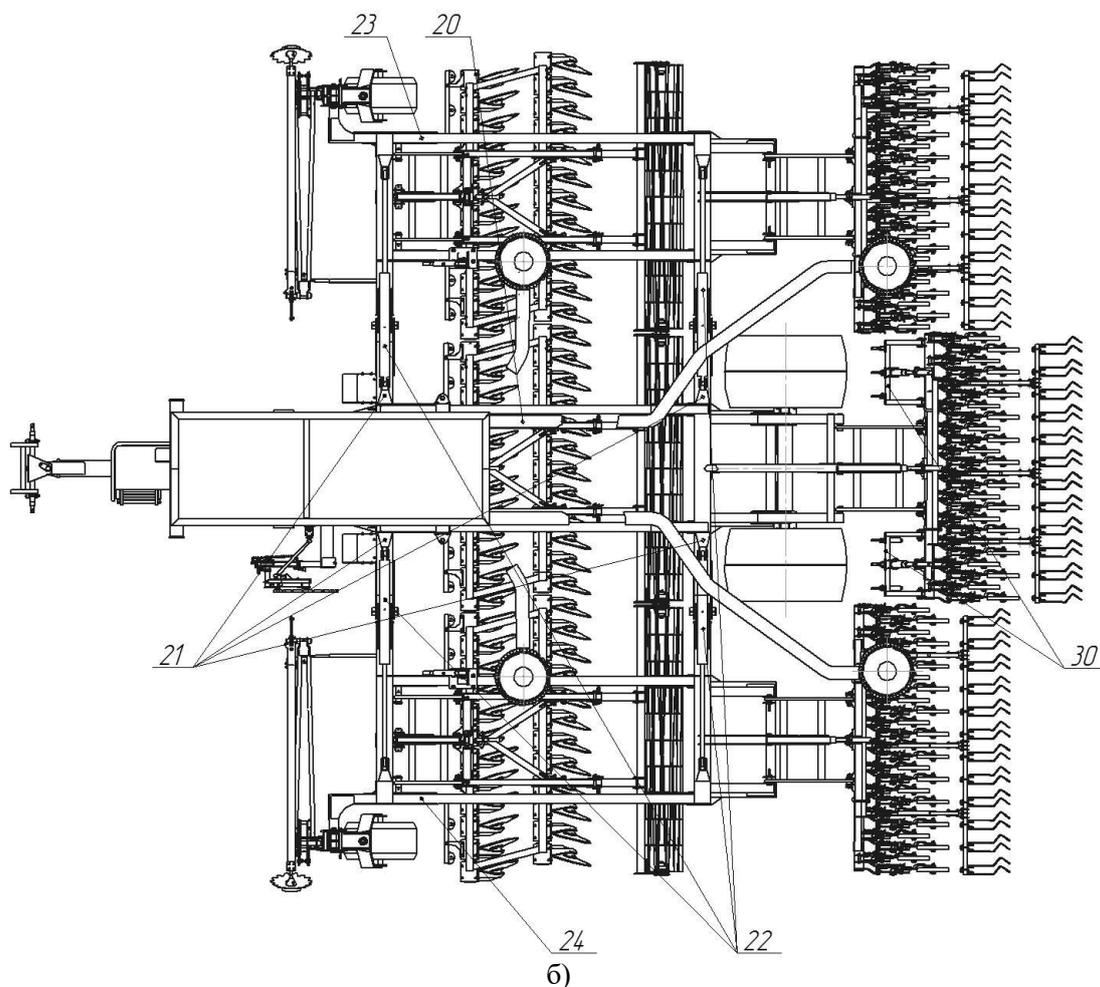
Конструктивная схема почвообрабатывающе-посевной агрегат АПП – 9
